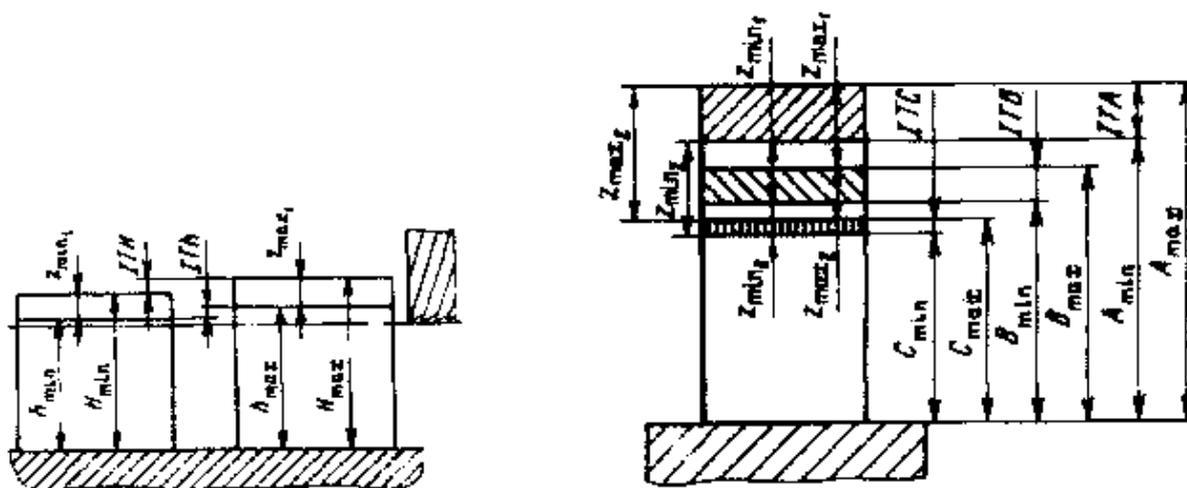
Схема промежуточных и исходных размеров заготовки и припусков при одной операции обработки заготовки
